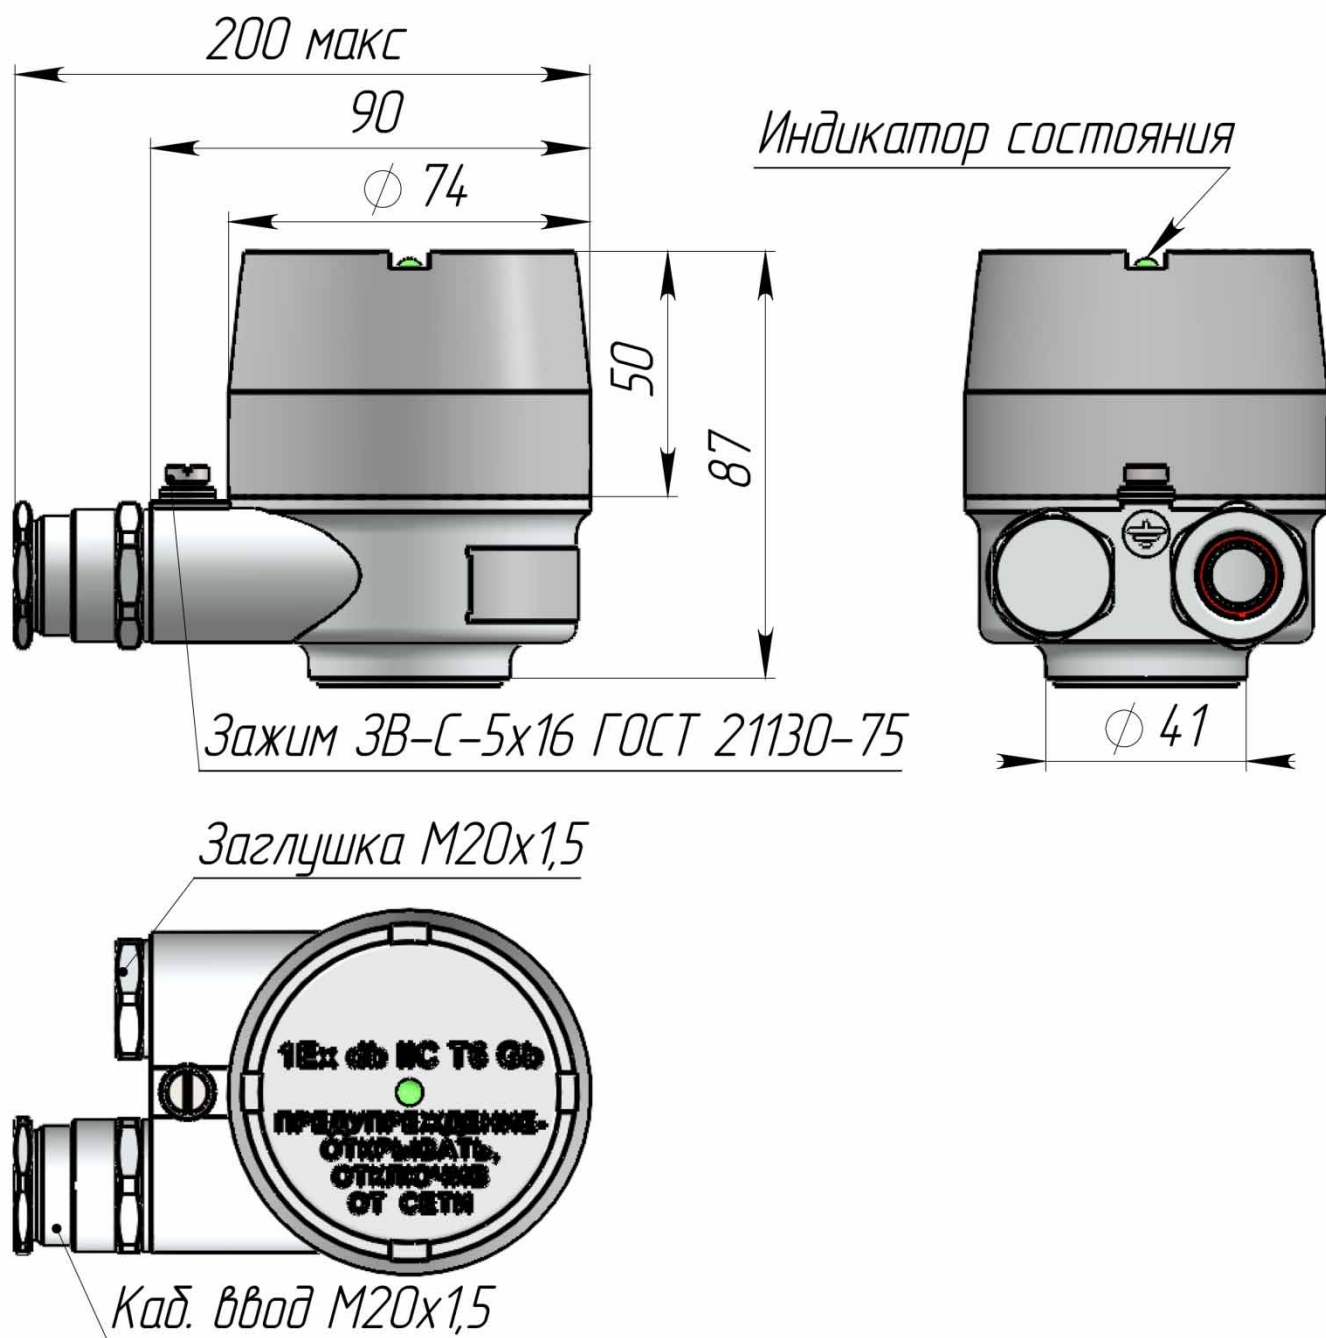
Габаритные размеры корпуса блока электронного в корпусе из нержавеющей стали для общепромышленного применения (высокая крышка)
